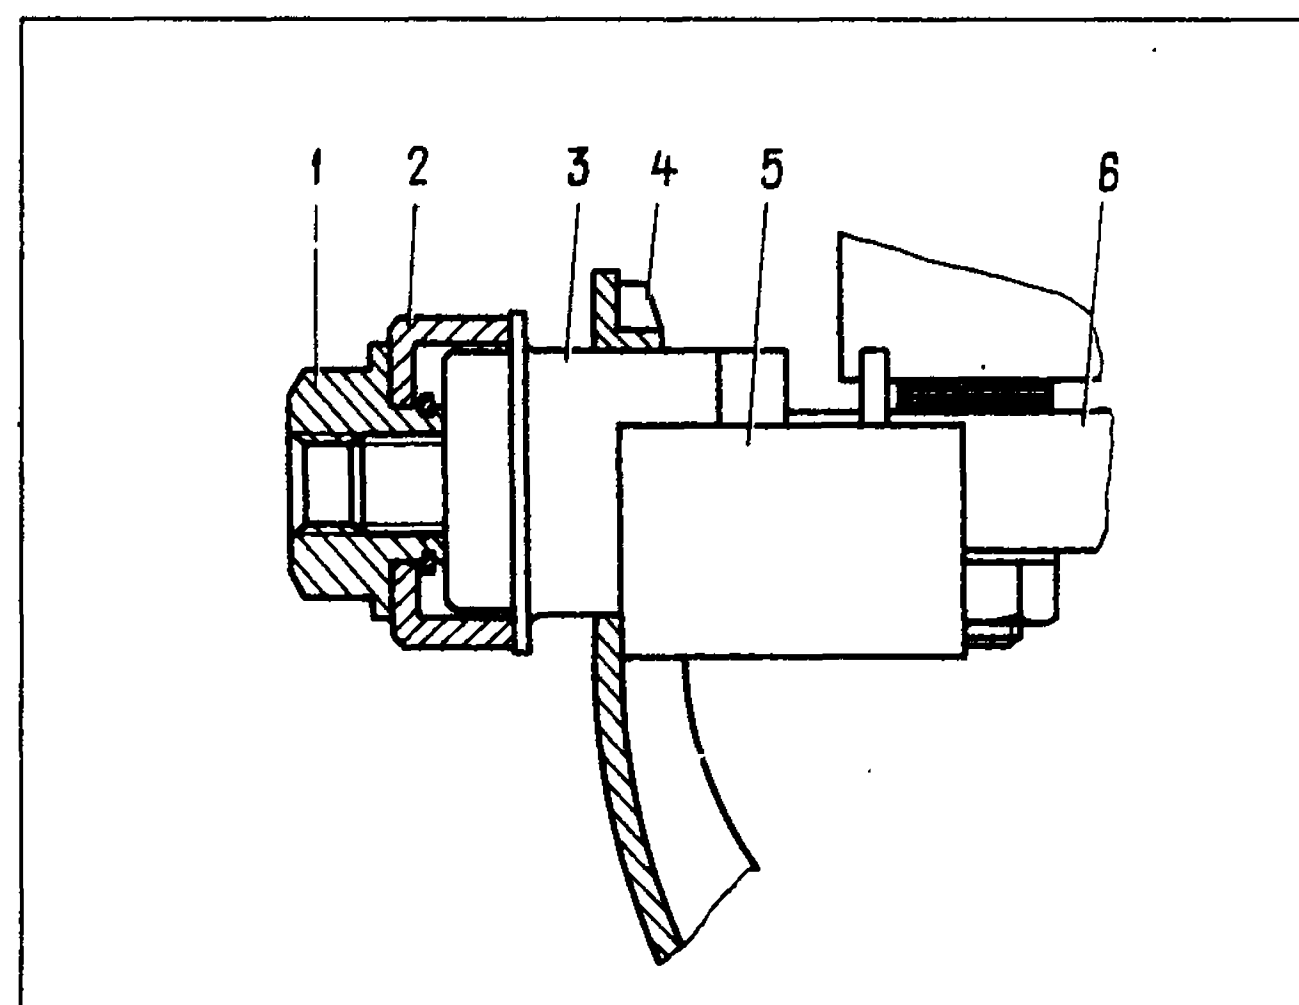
Схема запрессовки шарнира нижнего рычага с помощью приспособления 02.7823.9501: 1-гайка; 2-кольцо; 3-шарнир; 4-нижний рычаг; 5-упор; 6-ось нижнего рычага
